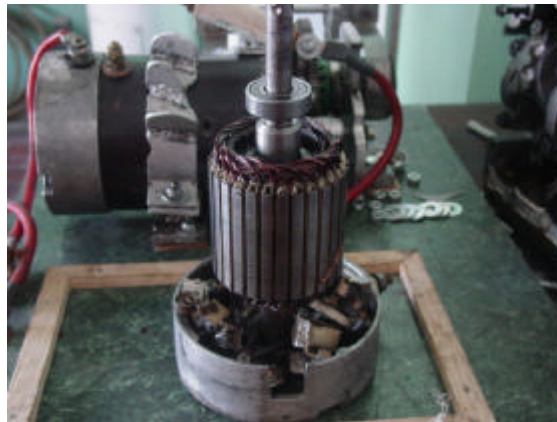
Desarme y mantenimiento del motor de 2 HP.
